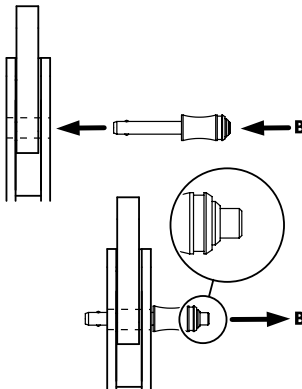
Locking Pins für die Splay/Rear Links der Lautsprecher, am Flugrahmen und an den Lastadaptern
